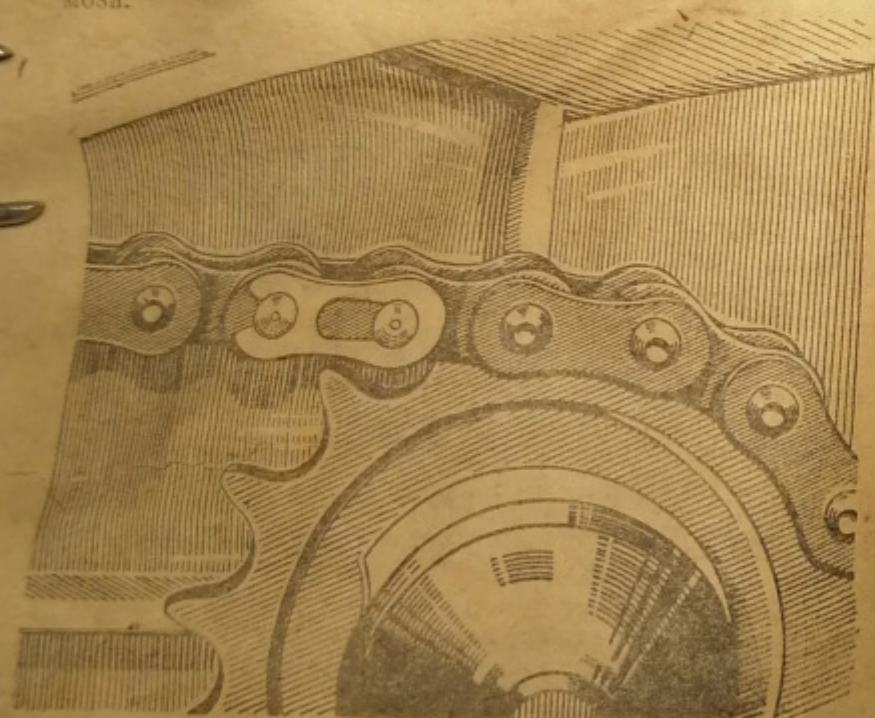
УСТАНОВКА ЗАЩЕЛКИ ЗАМКА ЦЕПИ
